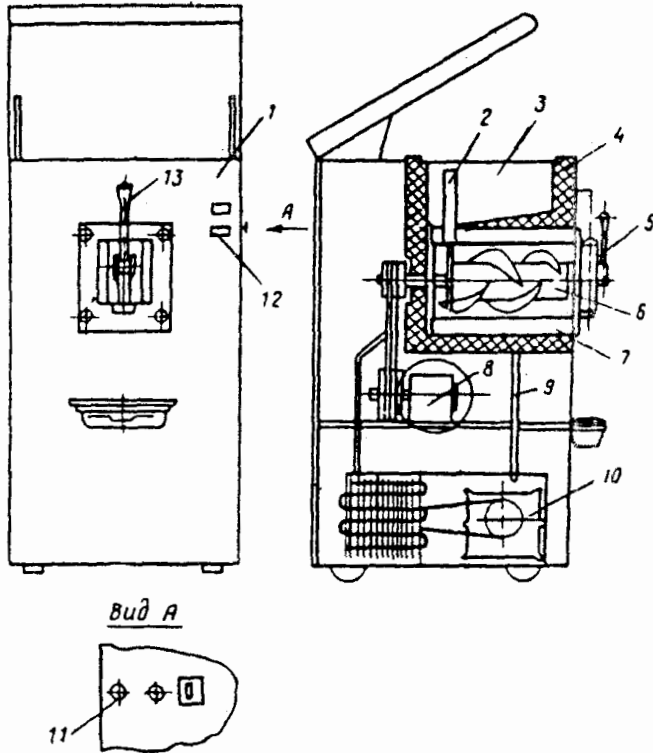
Фризер ФМ-1: 1 – корпус; 2 – дозатор; 3 – бак; 4 – теплоізоляція; 5 – добірний пристрій; 6 – мішалка; 7 – робочий циліндр; 8 – привод мішалки; 9 – трубопровід; 10 – холодильний агрегат; 11 – терморегулятор; 12 – шкала; 13 – рукоятка.
